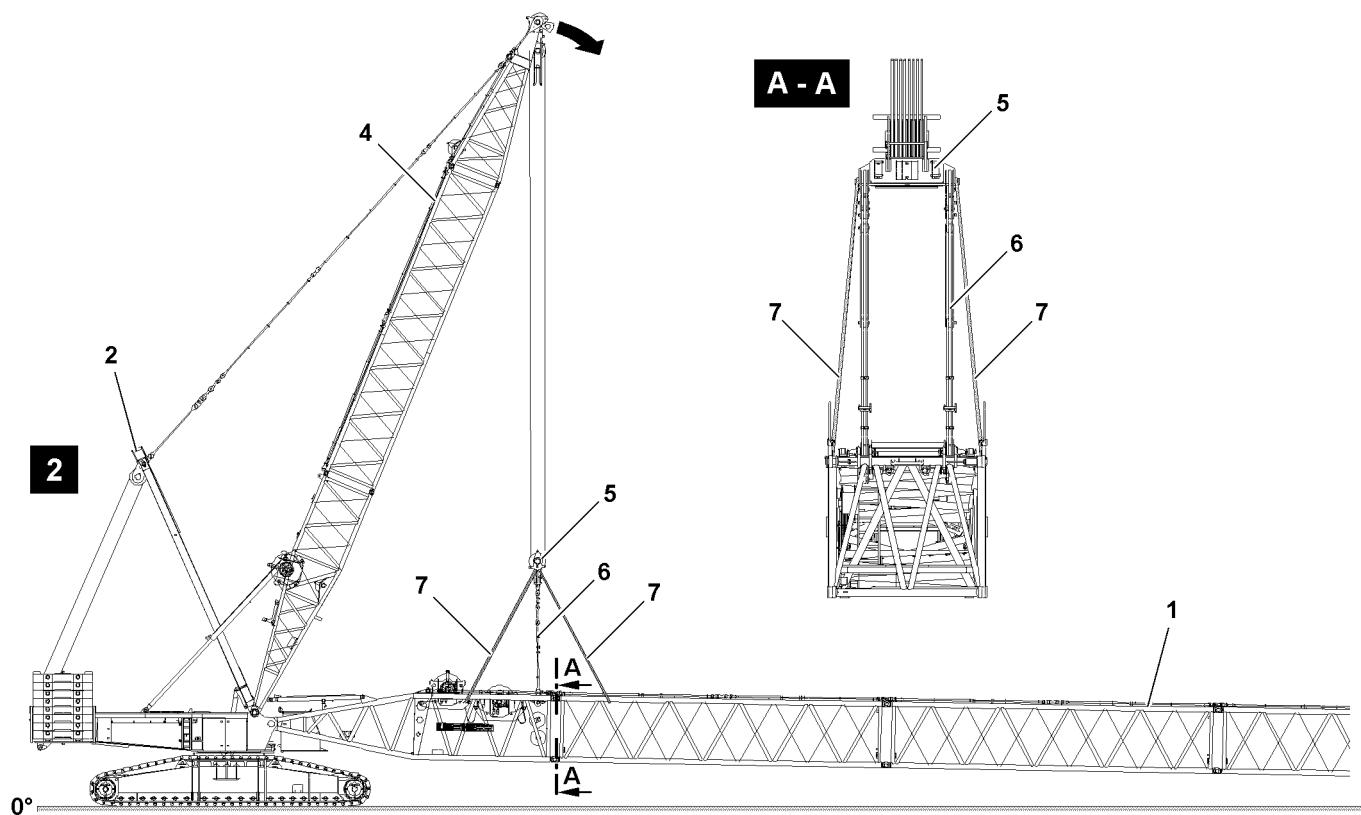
Anclaje apoyado en el soporte de transporte y pasteca superior amarrada a la pluma
